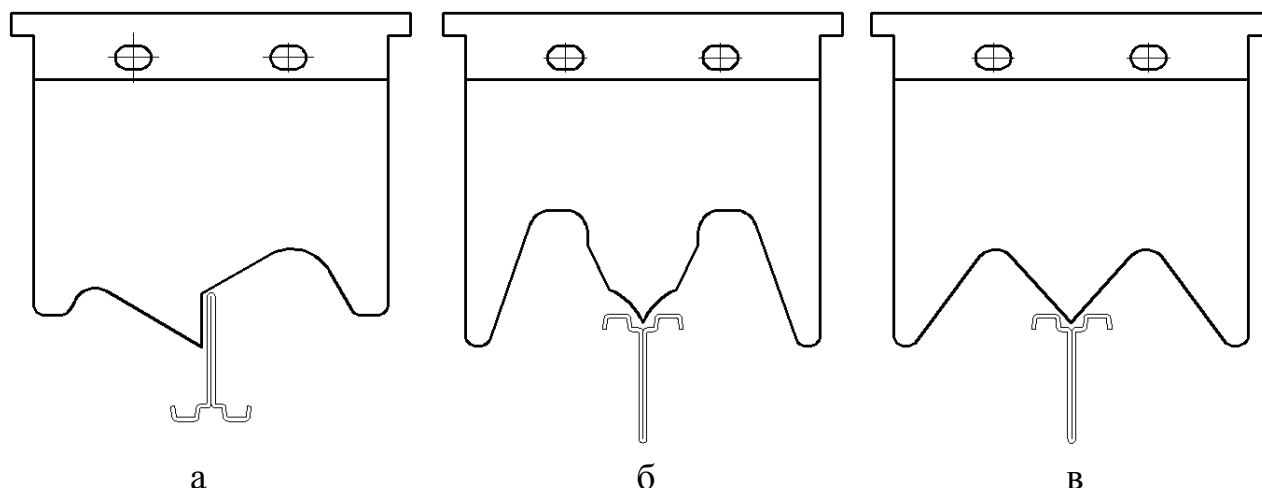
Варианты ножей для резки в штампе стандартным способом: а – нож со смещенным центром реза, б – нож конусный копьевидный, в – нож конусный
